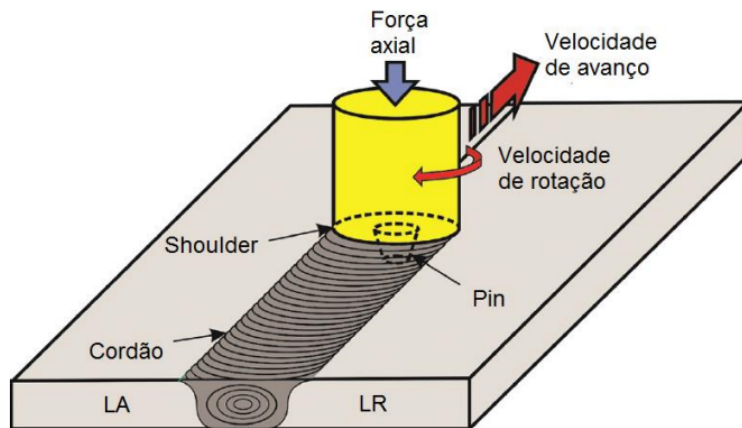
Descrição do processo de soldadura por fricção. Fonte: [12]
